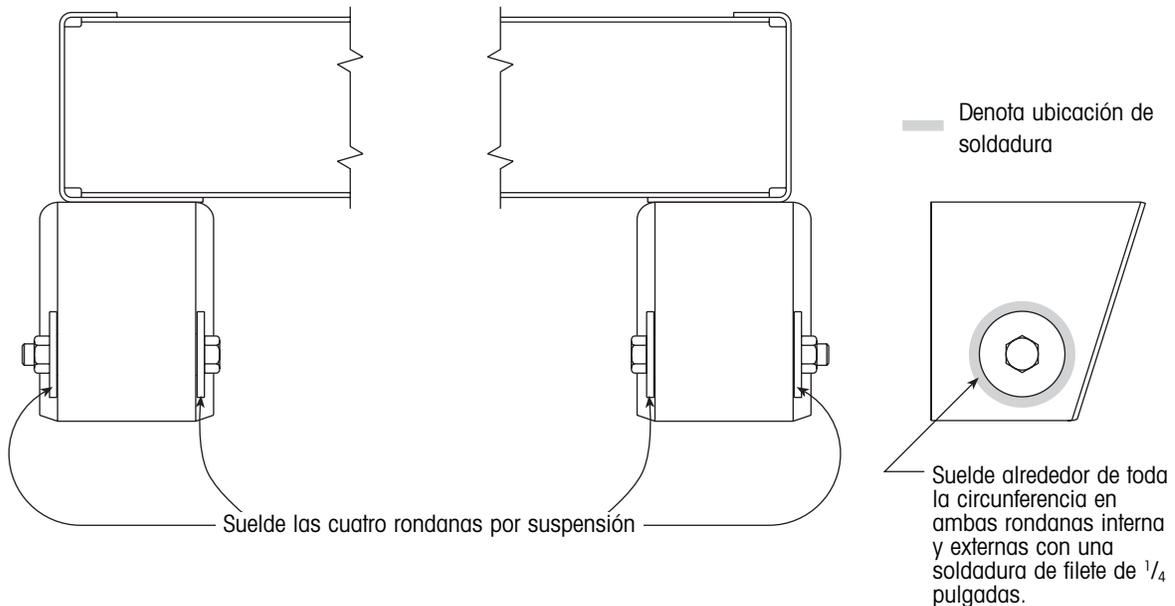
Ubicación de soldadura en rondana soldable
